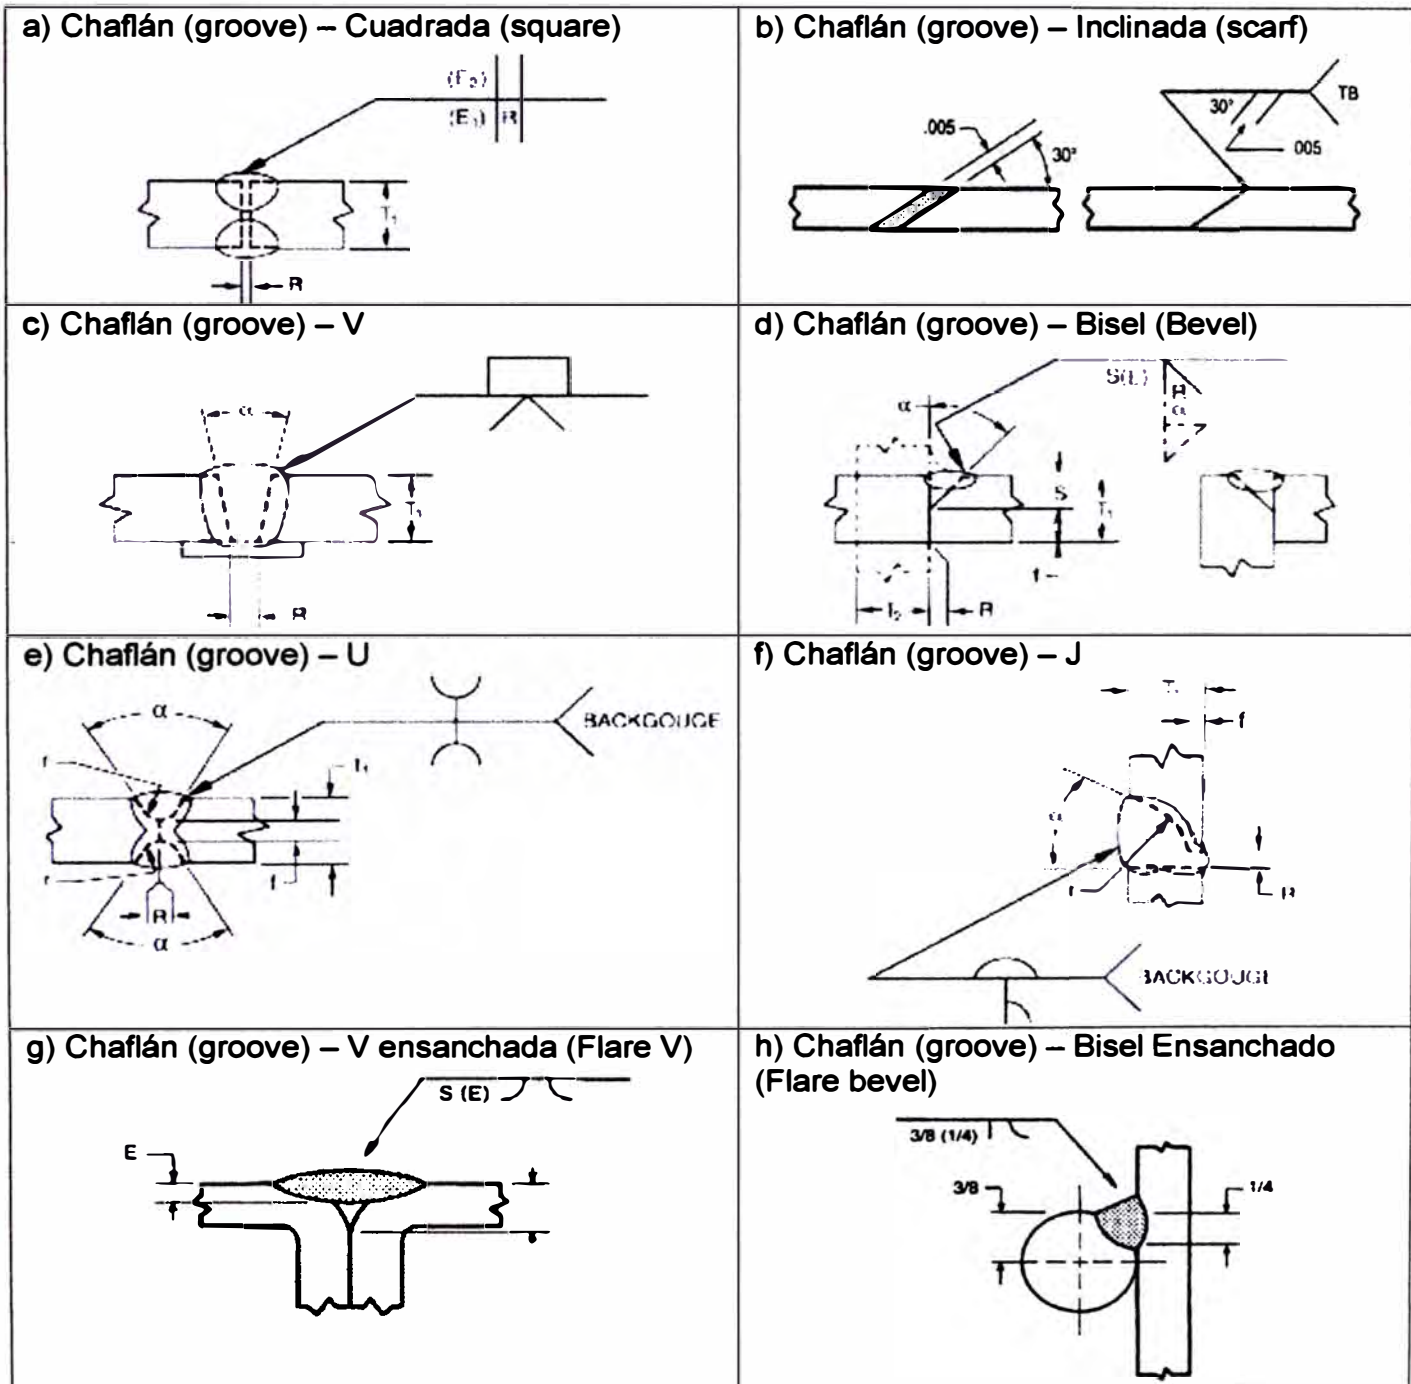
Tipos de Soldadura (Ver bibliografía N° 6)
